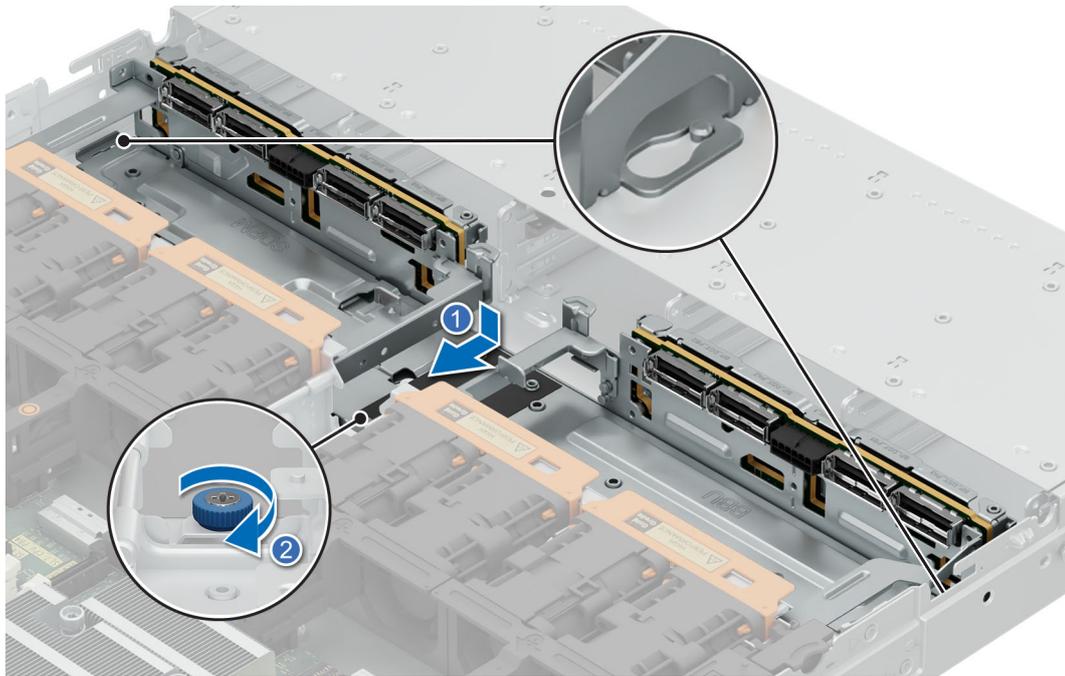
Installation d'un fond de panier de 14 disques E3.S
